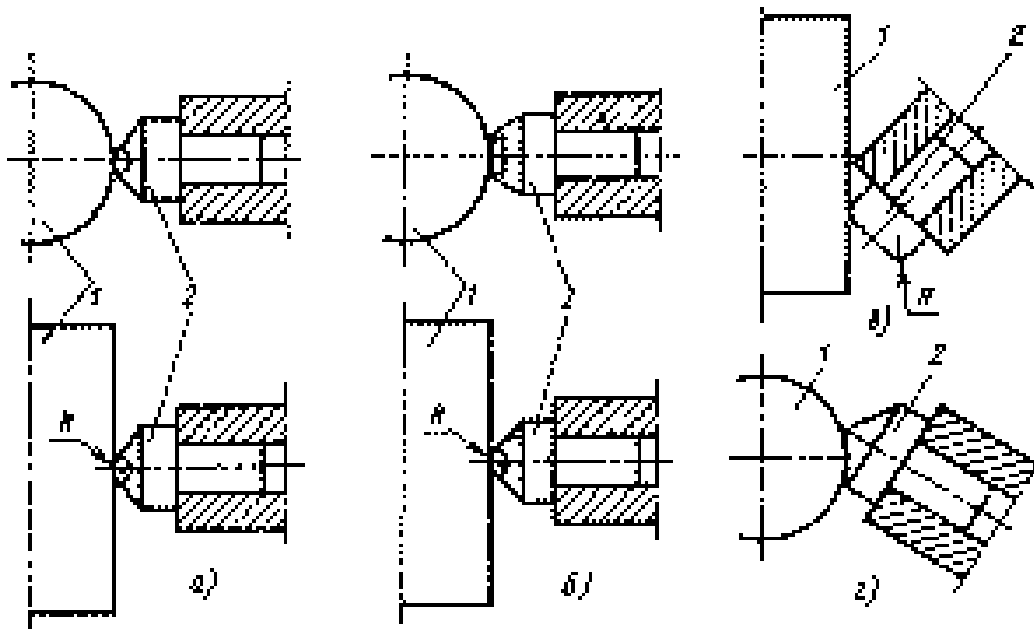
Схема установок вигладжувачів під час обробки циліндричної поверхні
